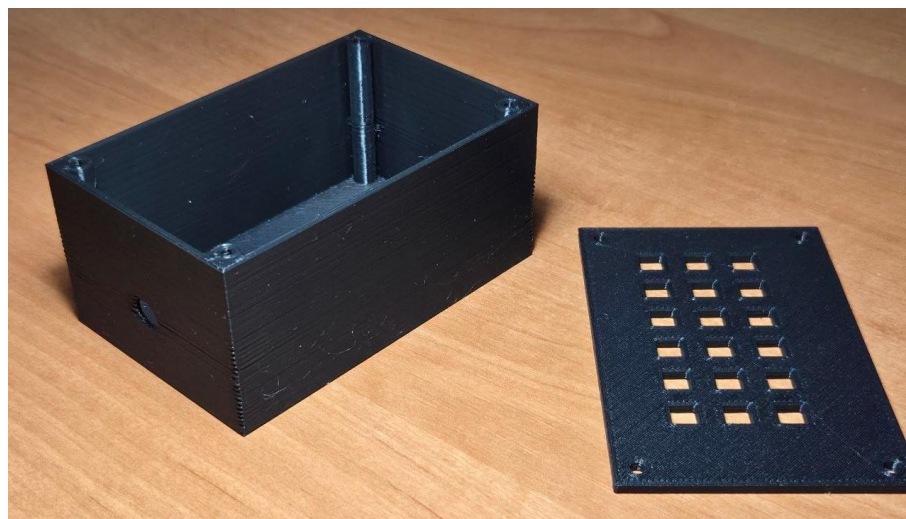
Основні деталі корпусу після етапу 3D-друку
